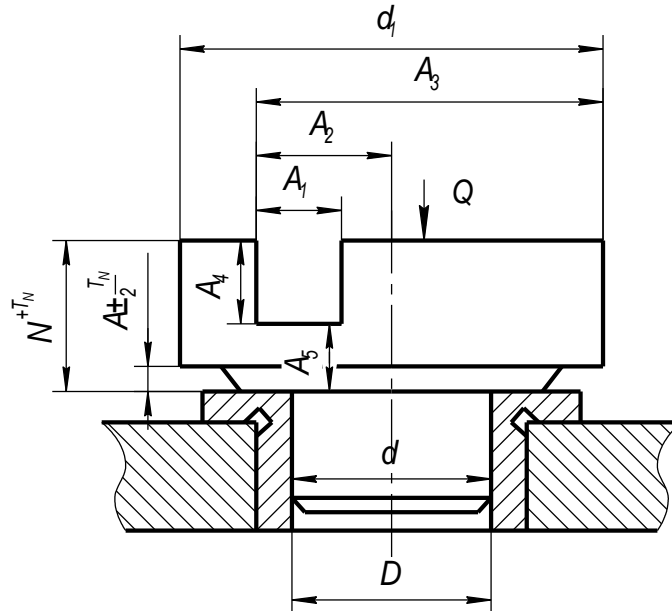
Схема установки заготовки при фрезеровании паза
